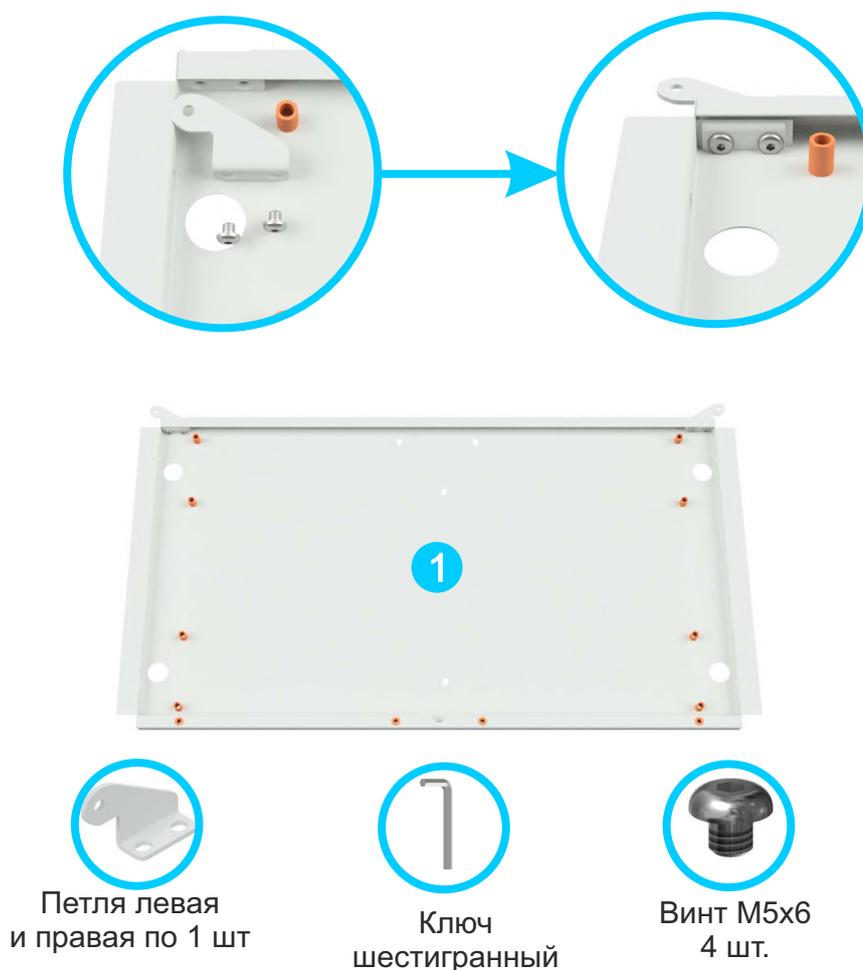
Установка петель в верхнюю и нижнюю крышки
